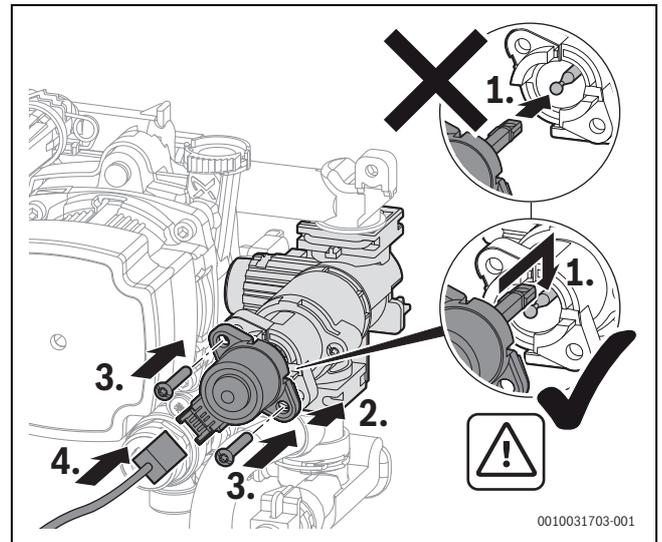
Motor am 3-Wege-Ventil einbauen (Variante mit Schrauben)
